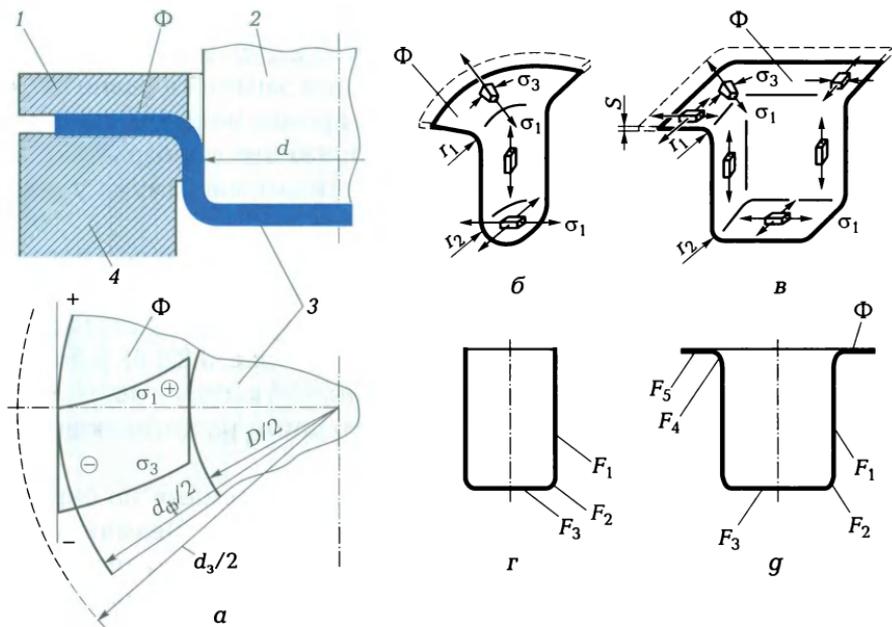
Распределение нормальных напряжений во фланце круглой заготовки при вытяжке из нее цилиндрической детали (а); напряженное состояние в различных зонах вытягиваемой заготовки (б — трубчатой; в — корычатой) и схемы к расчету размеров заготовок тел вращения без фланца (г) и с фланцем (д):
